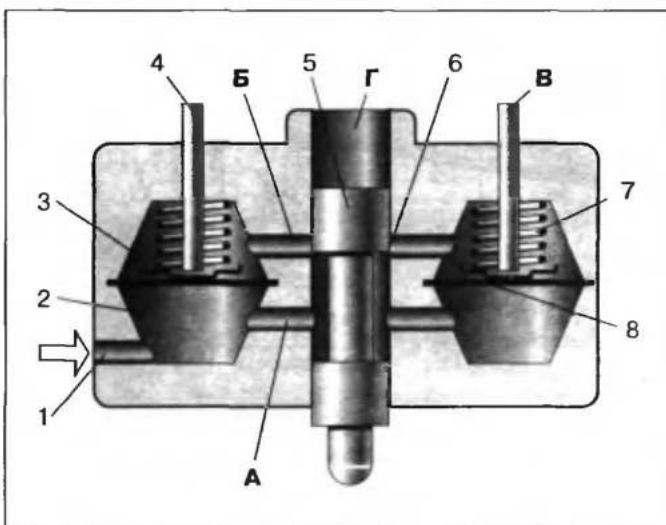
Конструкция дифференциальных клапанов: 1 — подвод топлива; 2 — нижняя камера; 3 — верхняя камера; 4 — канал подачи топлива к форсунке; 5 — дозирующий плунжер; 6 — рабочая кромка дозирующего плунжера; 7 — пружина; 8 — диафрагма; А — системное давление; Б — давление в верхней камере; В — давление на форсунке; Г — управляющее давление
